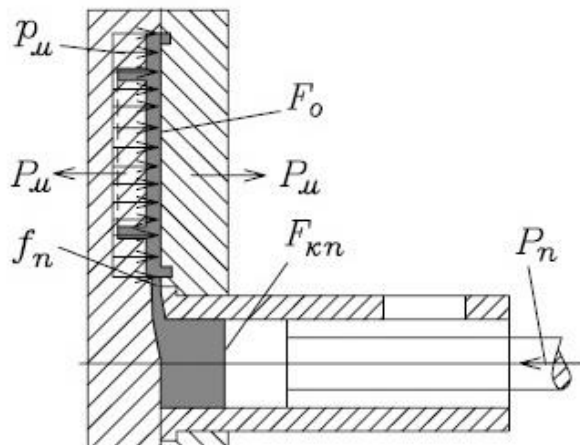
Схема заливки расплава в пресс-форму
